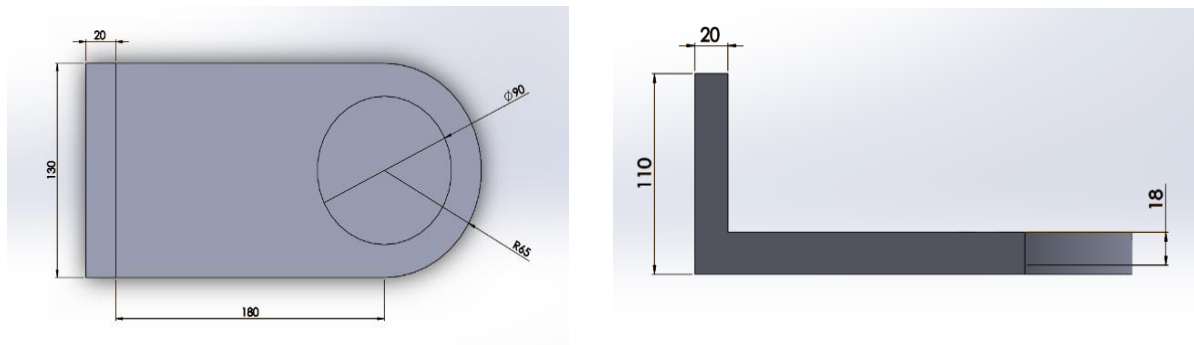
Dimensiones de la placa de apoyo del rodamiento inferior.
